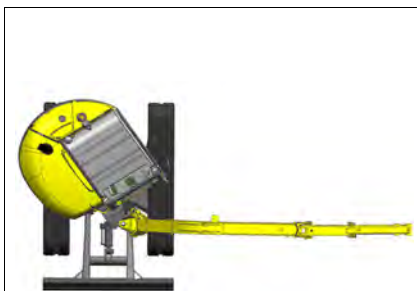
ET35 Posición del brazo ajuste de sobrecarga
